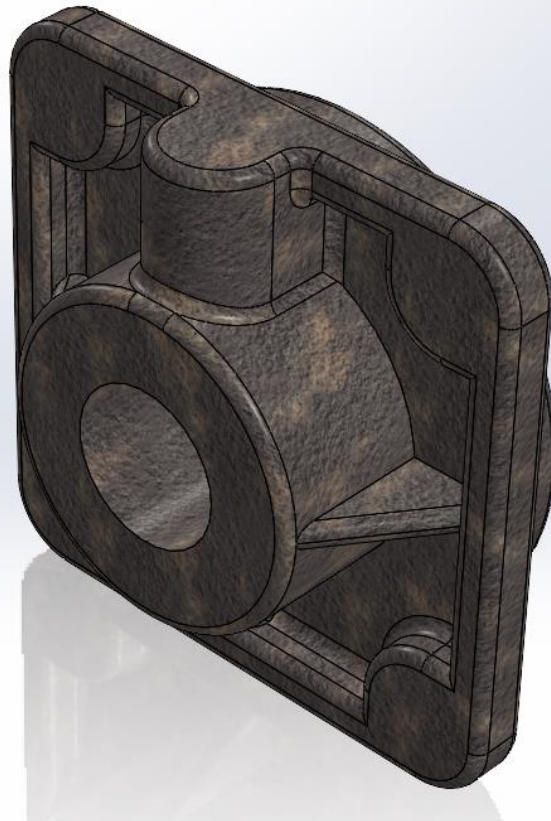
Виливок деталі «Кришка передня ПЦ 125-25.55»
